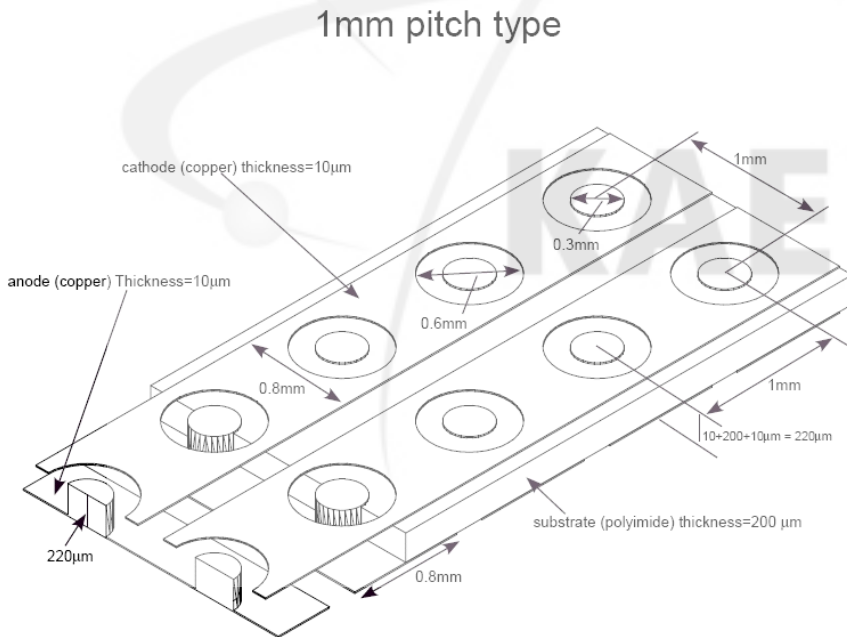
기체검출기에 사용되는 PCB 검출기의 전극구조 및 치수.
